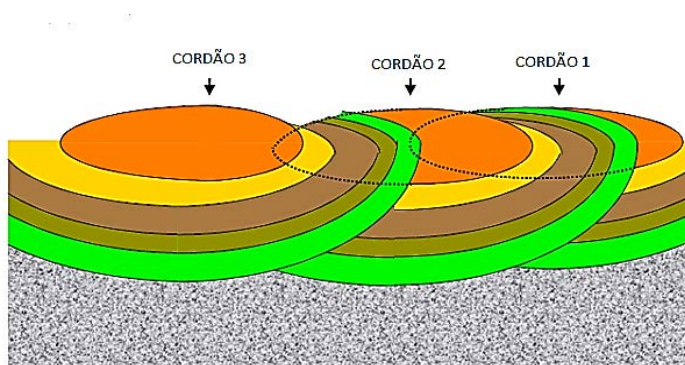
Representação do efeito da sobreposição de cordões subsequentes na extensão da ZTA pelo cordão de solda depositado previamente. – Exploring temper bead Welding. (Walter J) - Sperko – Welding Journal – July – 2005.
